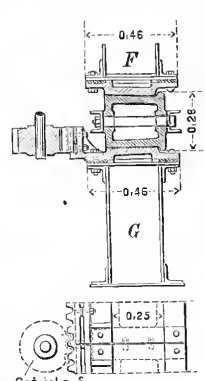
Rollkranz. Grundriß u. Schnitt.
